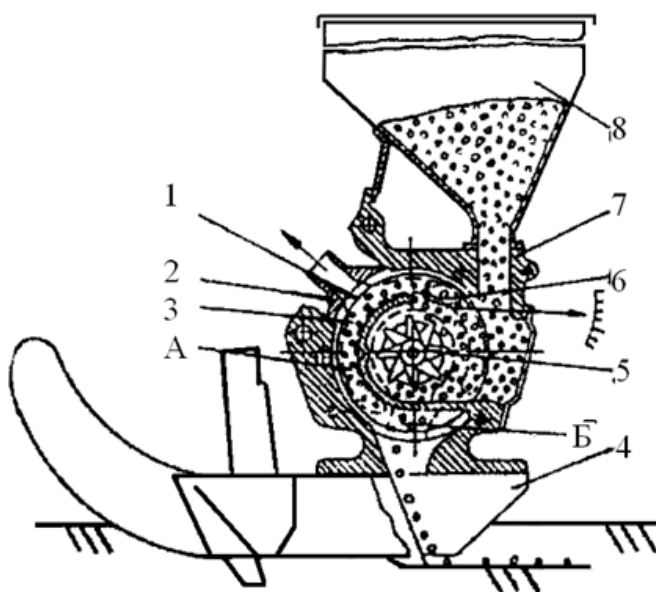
Схема пневмомеханічного висівного апарата: 1 – капронова вставка; 2 – кришка з камерою розрідження; 3 – висівний диск; 4 – комбінований сошник; 5 – ворушилка; 6 – скидач; 7 – корпус; 8 – бункер; А – зона розрідження; Б – зона атмосферного тиску.
